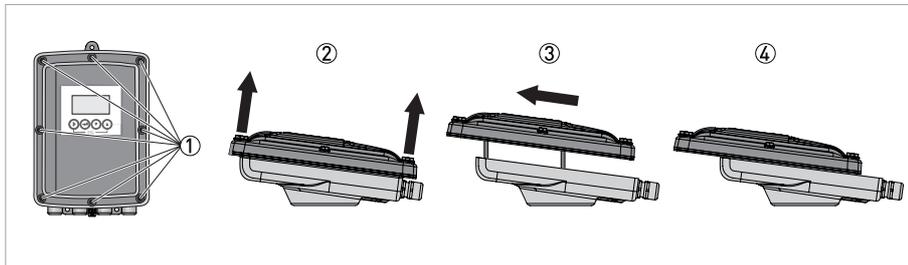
Открытие и закрытие корпуса из нержавеющей стали
